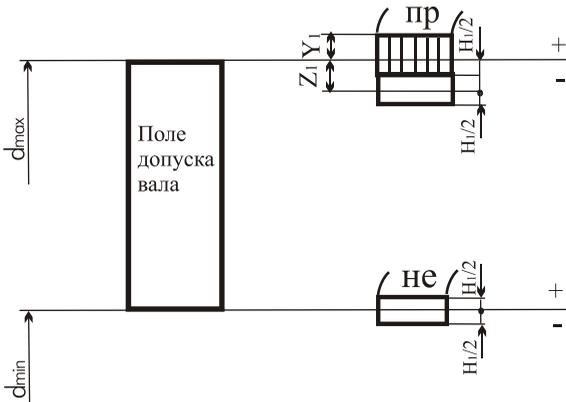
Схемы расположения полей допусков калибров
